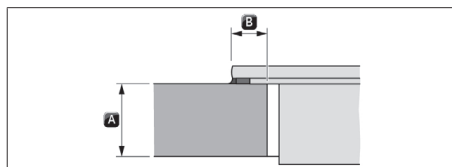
Dimensiones de cobertura para montaje superpuesto
